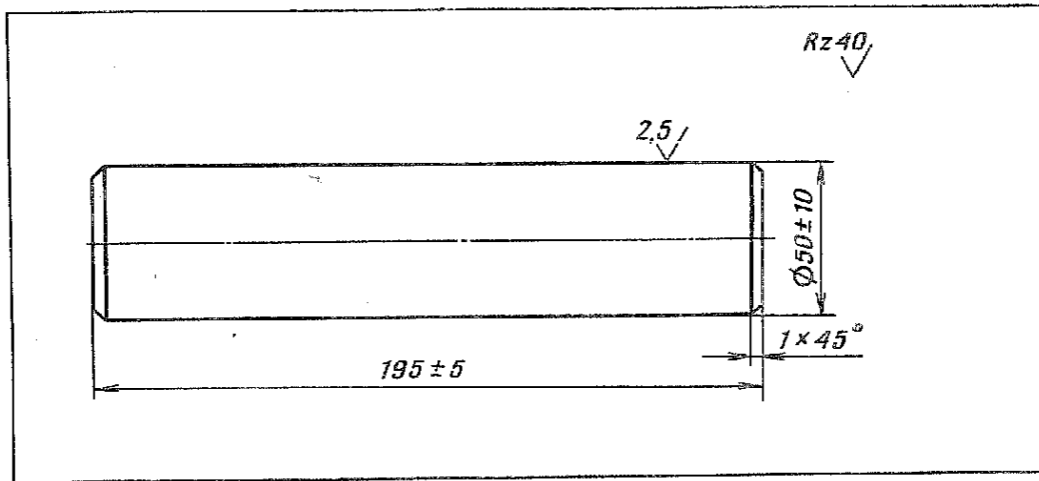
Оправка для определения регулировочных прокладок под подшипник ведущей шестерни главной передачи
